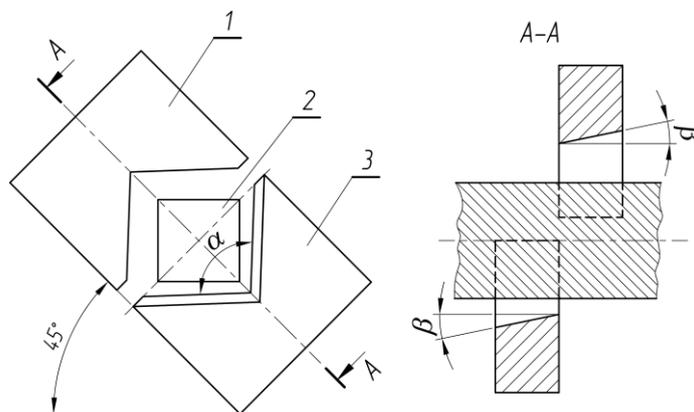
Схема установки гидравлических ножниц сортовой МНЛЗ: 1 – разрезаемая заготовка; 2, 3 – фасонные ножи
